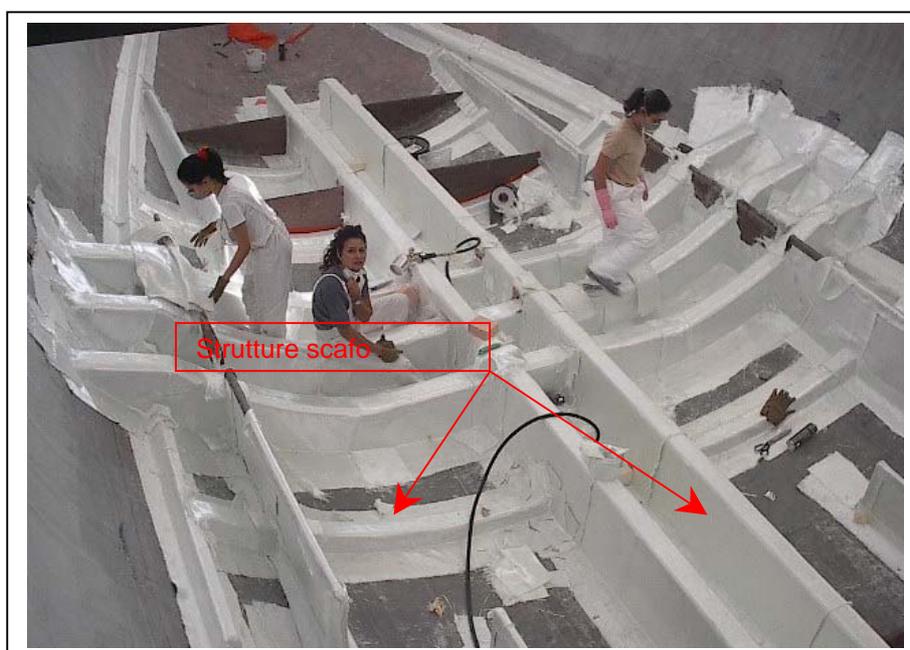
REALIZZAZIONE DELLE STRUTTURE
